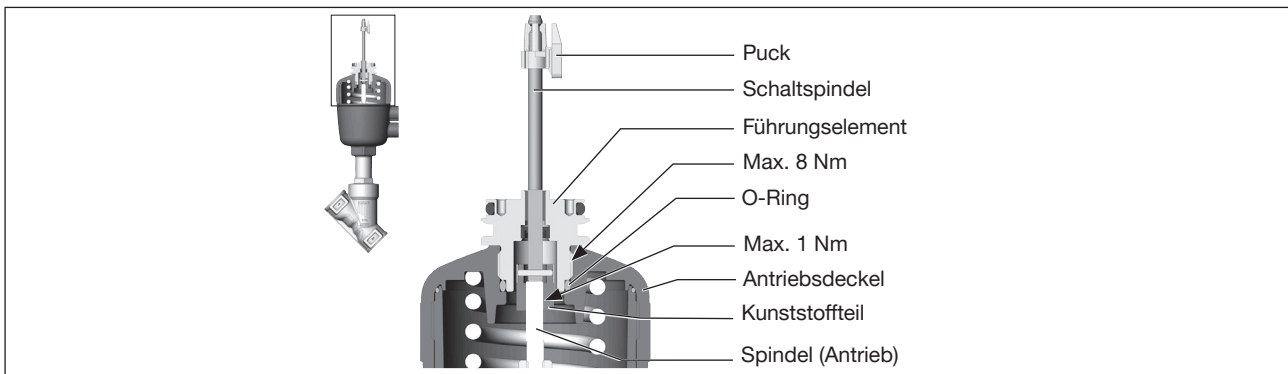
Schaltspindel montieren (2), externe Steuerluftführung
